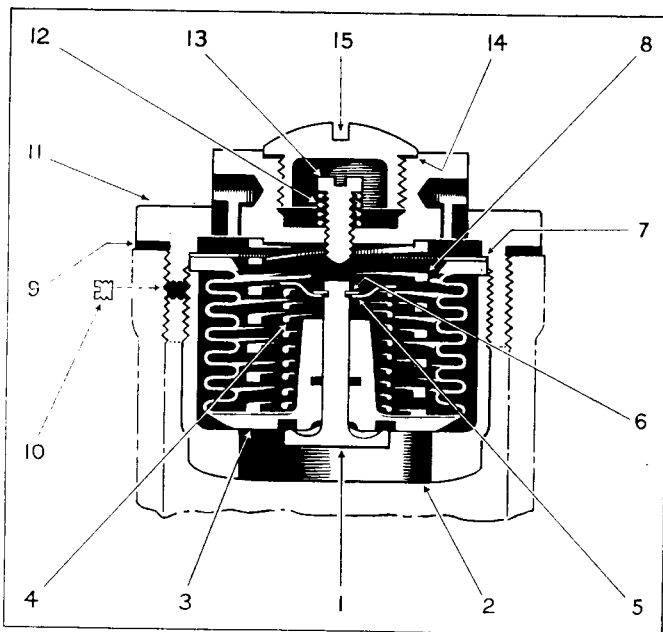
Нагнетательный клапан в сборке. (Радиатор в сборке).
